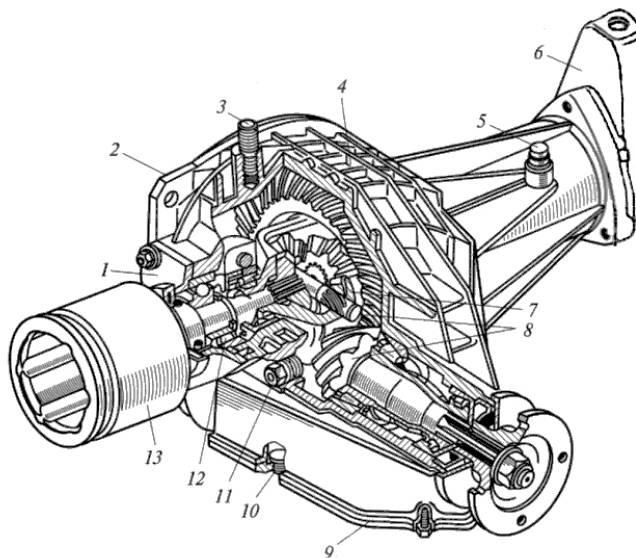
Передний ведущий мост автомобиля повышенной проходимости ВАЗ: 1, 2, 9 — крышки; 3 — шпилька; 4 — картер; 5 — сапун; 6 — кронштейн; 7 — дифференциал; 8 — главная передача; 10, 11 — пробки; 12 — подшипник; 13 — шарнир
